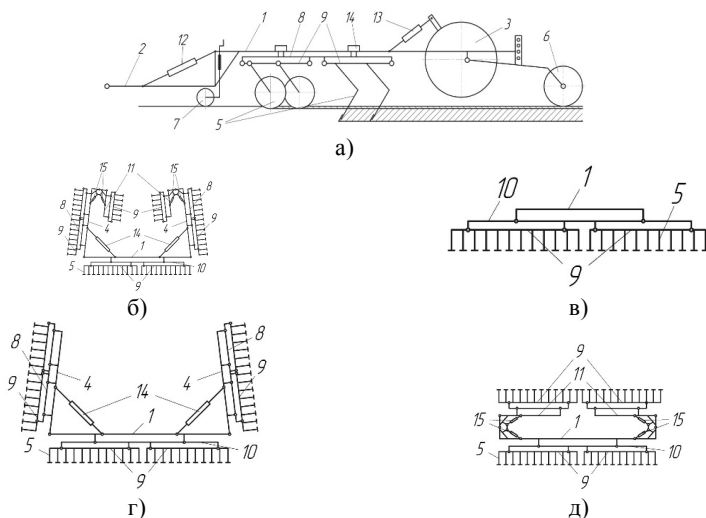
Схема почвообрабатывающего агрегата с изменяемой шириной захвата: а – агрегат, вид сбоку; б – агрегат с присоединенными боковыми и периферийными боковыми секциями, вид сзади; в – агрегат с отсоединенными боковыми секциями, вид сзади; г – агрегат с присоединенными боковыми секциями, вид сзади; д – агрегат с периферийными секциями, вид сзади; 1 – рама; 2 – сннца; 3 – транспортная тележка; 4 – боковая секция; 5 – почвообрабатывающие органы; 6 – каток; 7 – опорные колеса; 8 – заменяемый модуль; 9 – сменный подмодуль; 10 – средняя секция; 11 – периферийная секция; 12, 13, 14, 15 – гидроцилиндр
